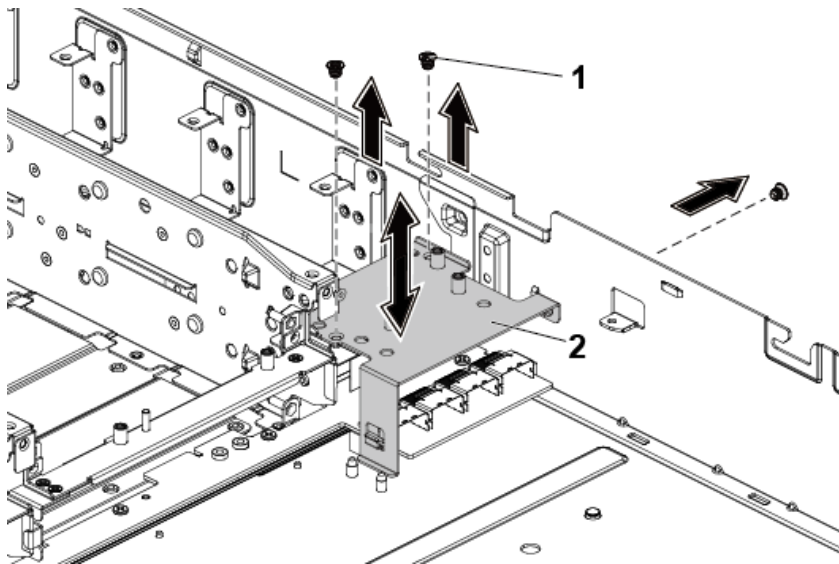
Entfernen und Einbauen der Mittelplattenhalterung
